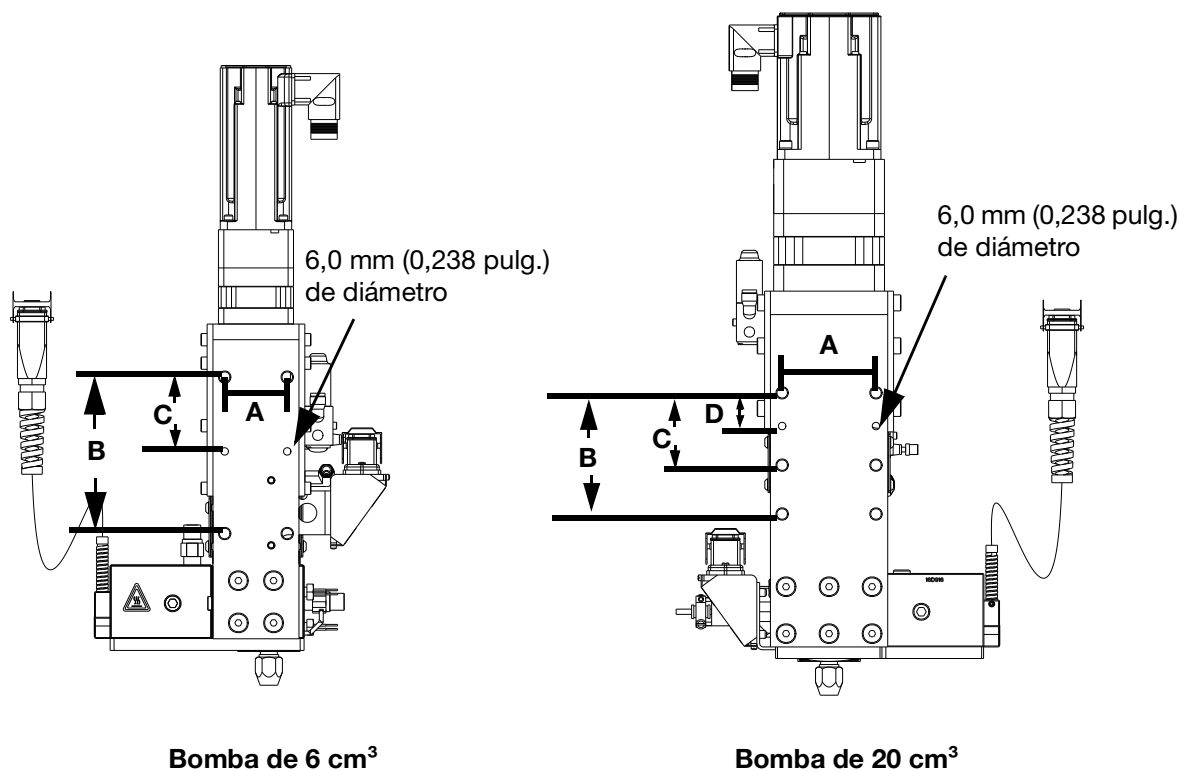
Dimensiones del conjunto del medidor de engranajes
